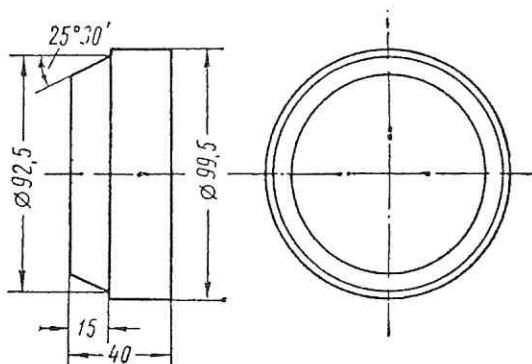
Оправка для запрессовки наружных колец подшипников вала
